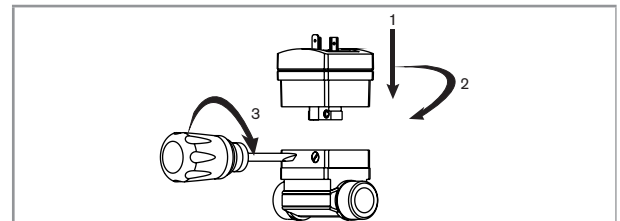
Montage des SE30 HT auf das Sensor-Fitting S030 HT
